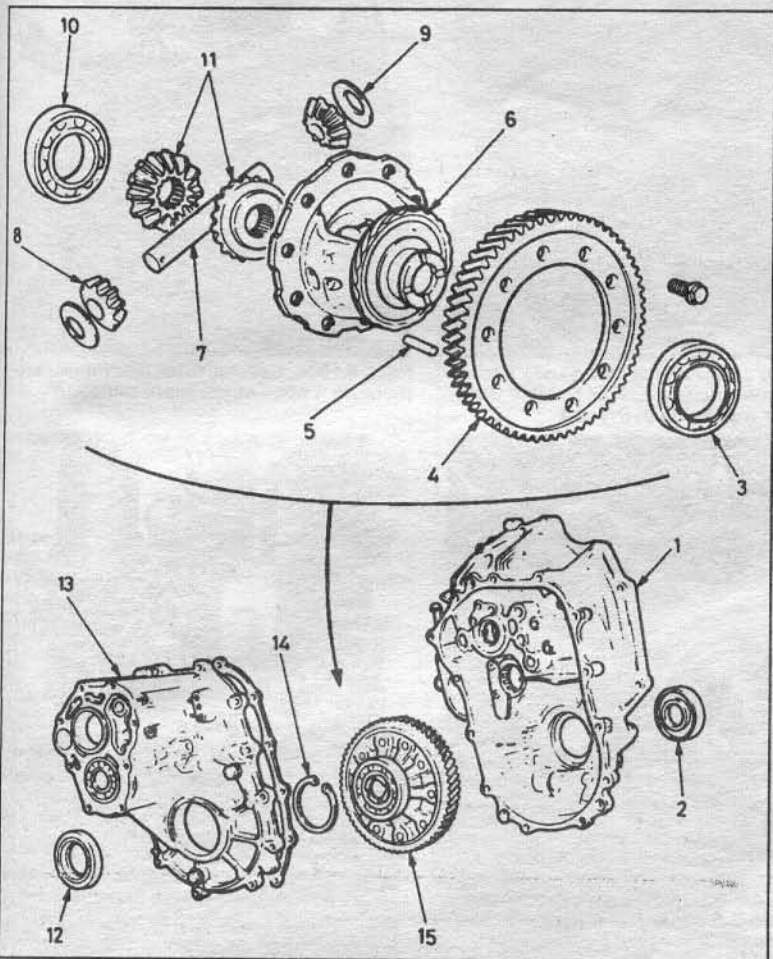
Сборка узла дифференциал/главная передача. 1 - картер сцепления; 2 - сальник; 3 - подшипник; 4 - ведомая шестерня главной передачи; 5 - штифт; 7 - вал ведущей шестерни; 8 - ведущая шестерня; 9 - упорная шайба; 10 - подшипник; 11 - боковая шестерня; 12 - сальник; 13 - корпус коробки; 14 - стопор; 15 - дифференциал в сборе.
